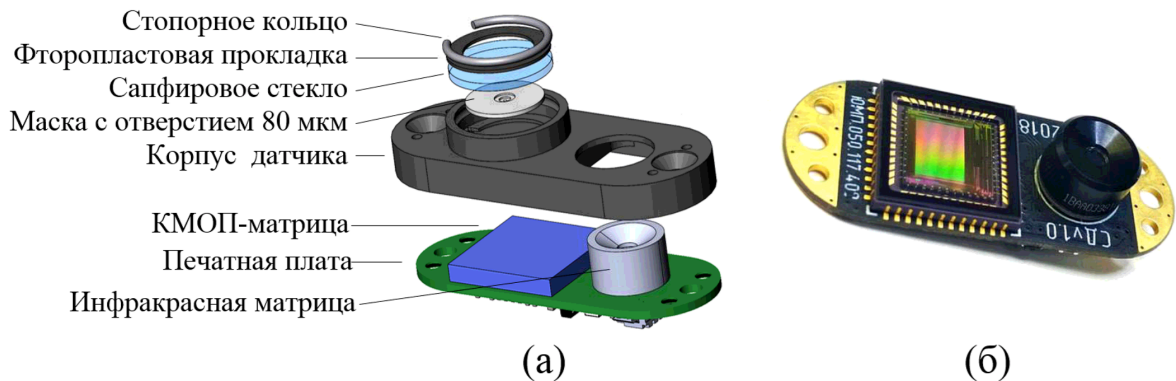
Конструкция датчика ДСГ: 3D-модель (а) и фотография опытного образца без корпуса (б).
